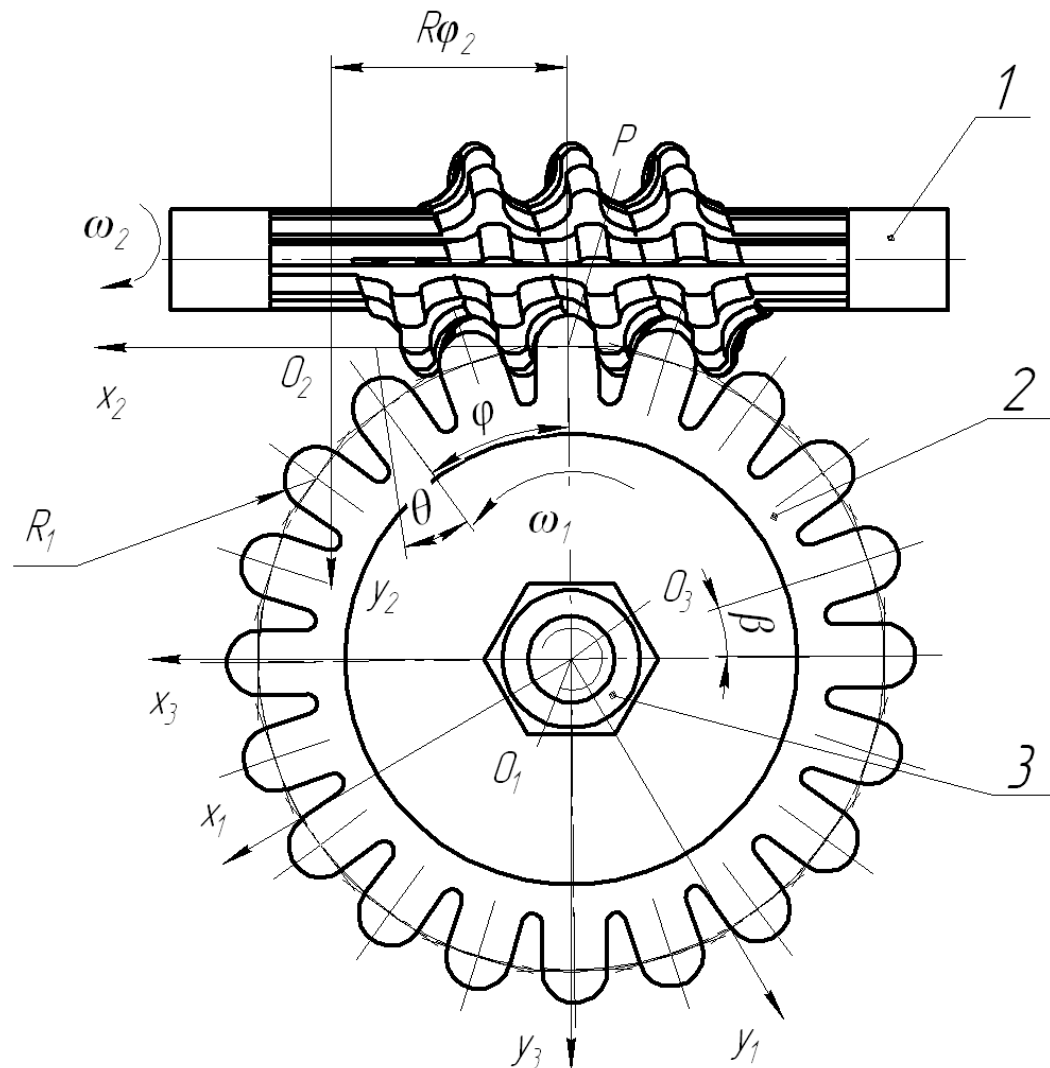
Розрахункова схема для визначення профілю робочої частини черв'ячної фрези: 1 – профільна черв'ячна фреза, 2 – заготовка із радіусними поверхнями; 3 – пристрій для затиску і базування заготовки
